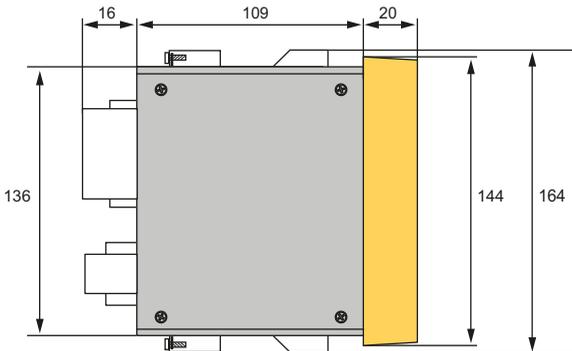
Maßbild PEM735 (Seitenansicht)
